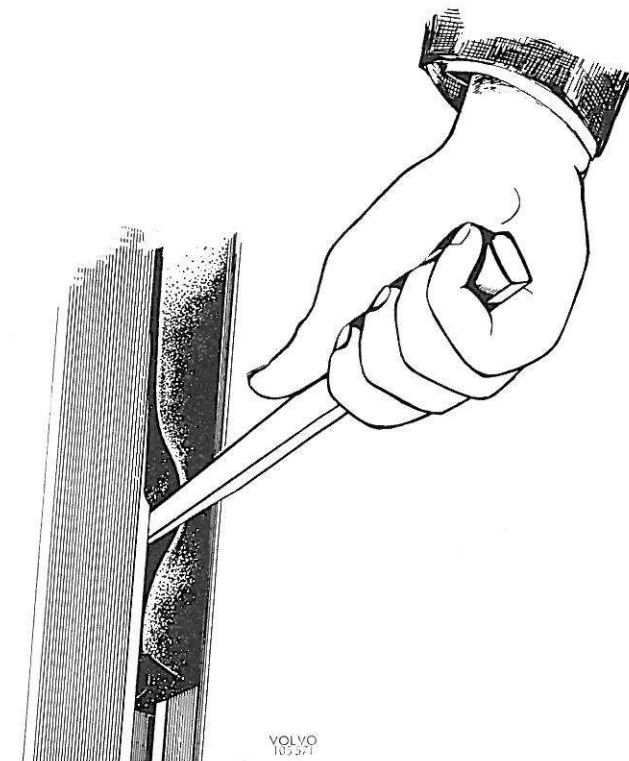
Démontage d'un joint d'étanchéité d'encadrement de porte
